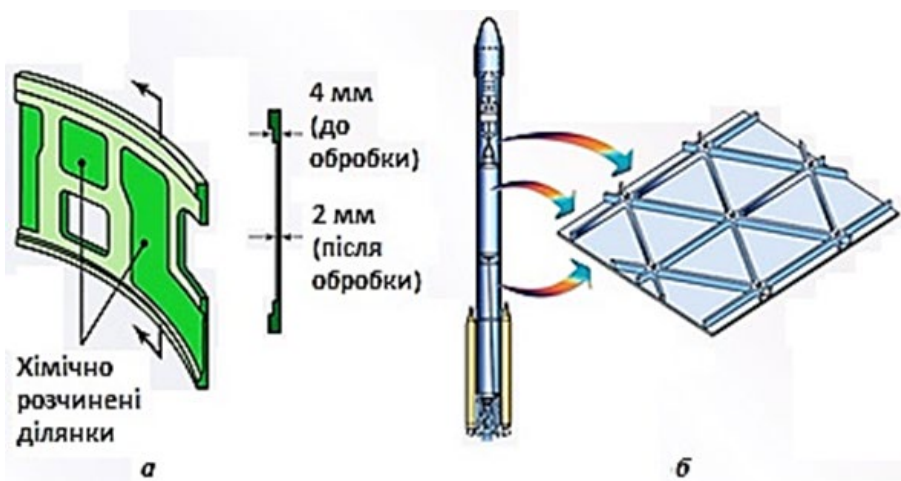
Виготовлення ребристих оболонок – елементів корпусу ракети
